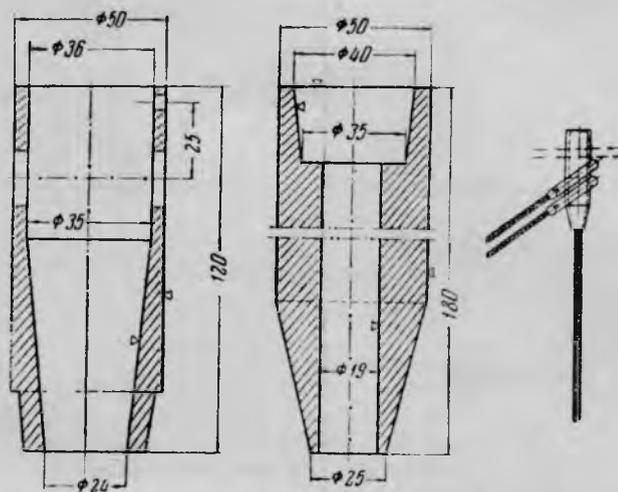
Стопорная головка (слева — стопорная головка в разрезе, справа — собирающий трос в сборе со стопорной головкой)
